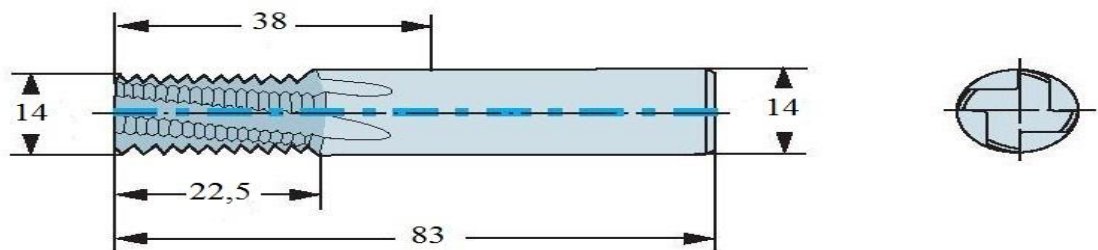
Резьбовая фреза M14x1,5 CoroMill R217–14C120150AC22N
